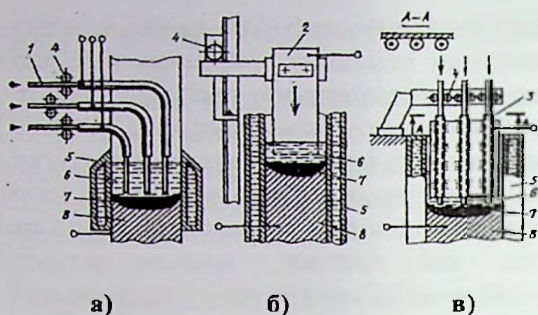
Способы электрошлаковой сварки:
